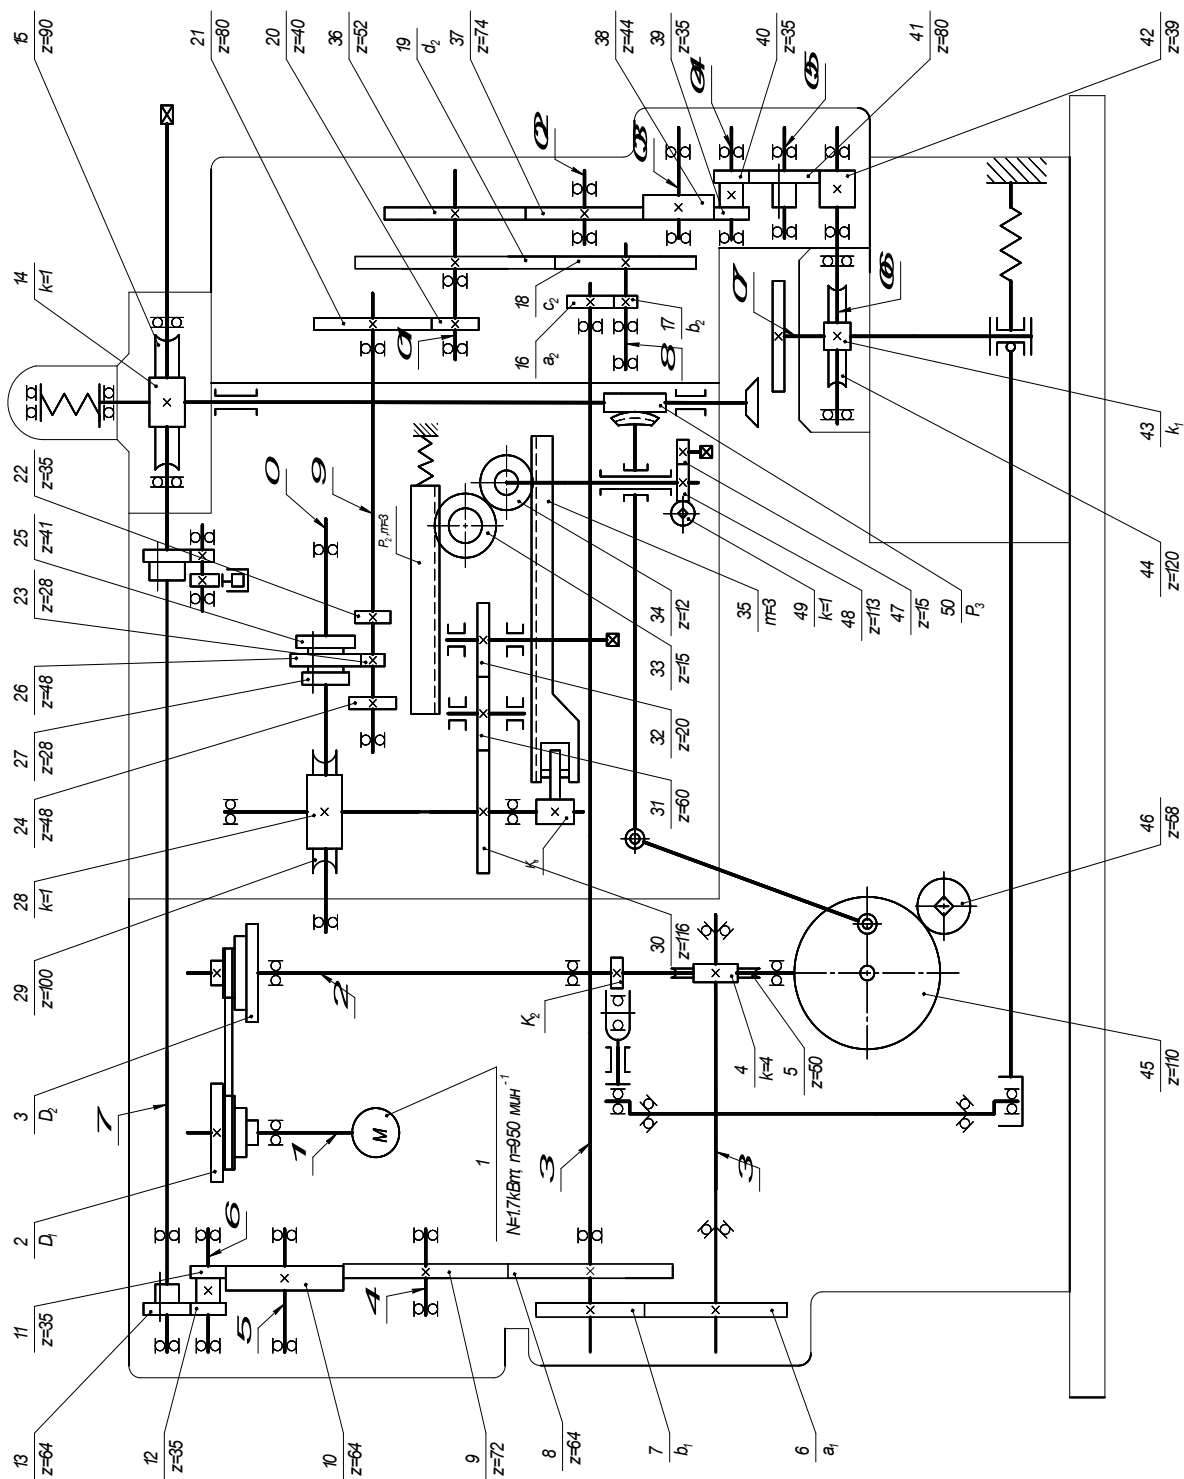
Кинематическая схема зубодолёжного станка модели 5B12
